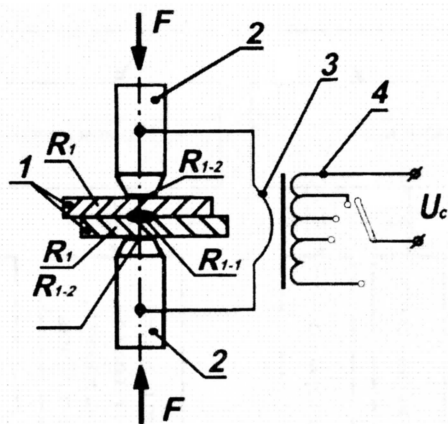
Схема контактной сварки: 1 — свариваемые заготовки; 2 — электроды; 3 — вторичная обмотка трансформатора; 4 — первичная обмотка трансформатора
